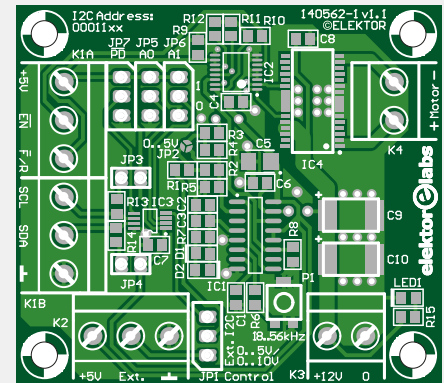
Leer und bestückt: die kleine Platine der Motorsteuerung.
